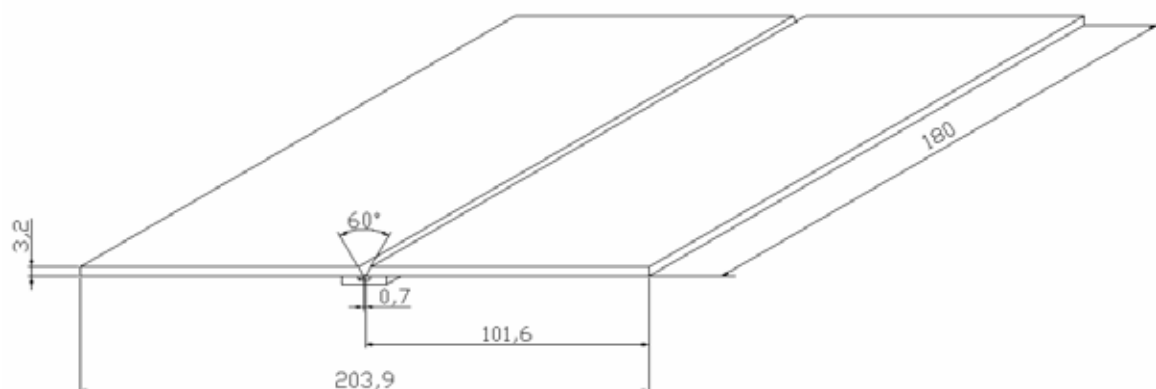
Geometria e principais dimensões da junta utilizada.
